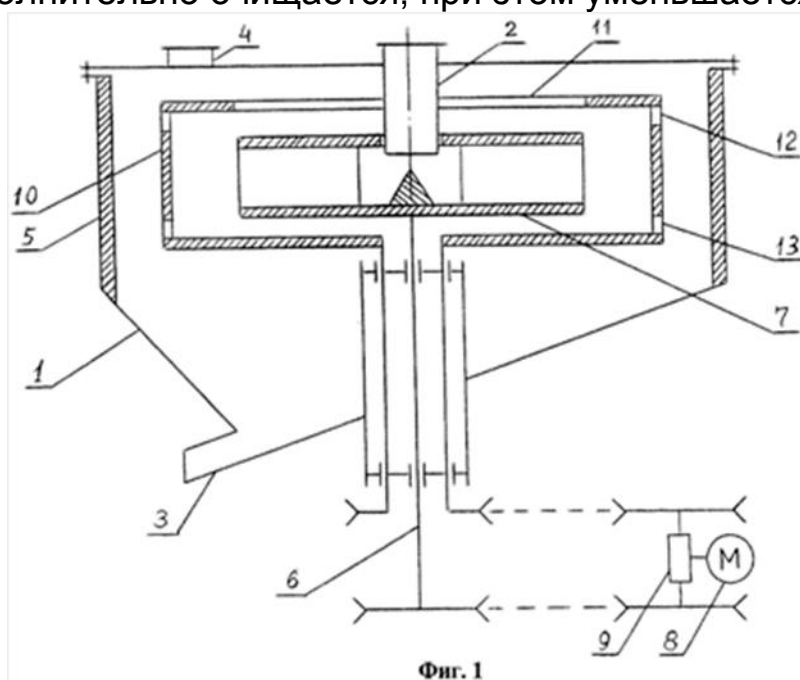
Устройство для шелушения зерна (патент РФ 2457904)
